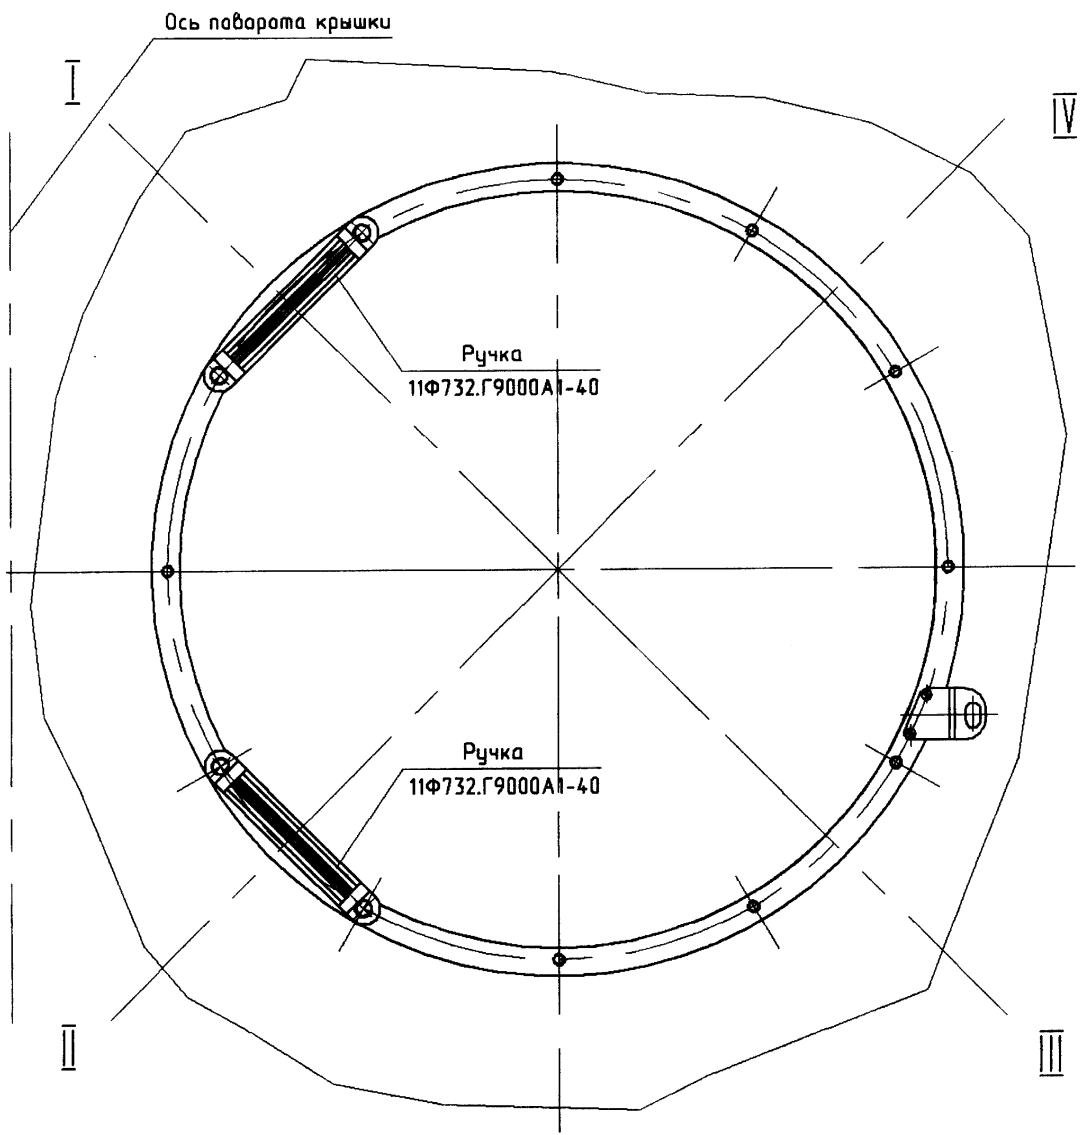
Схема установки ручек 11Ф732.Г9000А1-40 после демонтажа стыковочного механизма на крышку люка 11Ф732.9000А1-0
